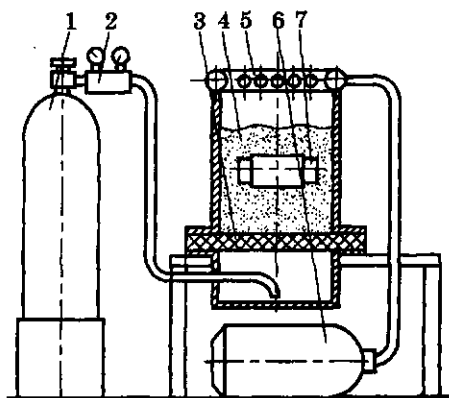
Установка для нанесения пластмассовых покрытий в слое, содержащем взвешенные частицы пластмассы: 1 — баллон; 2 — редуктор давления; 3 — пористая перегородка; 4 — камера; 5 — вытяжное устройство; 6 — пылесос; 7 — восстанавливаемая деталь
